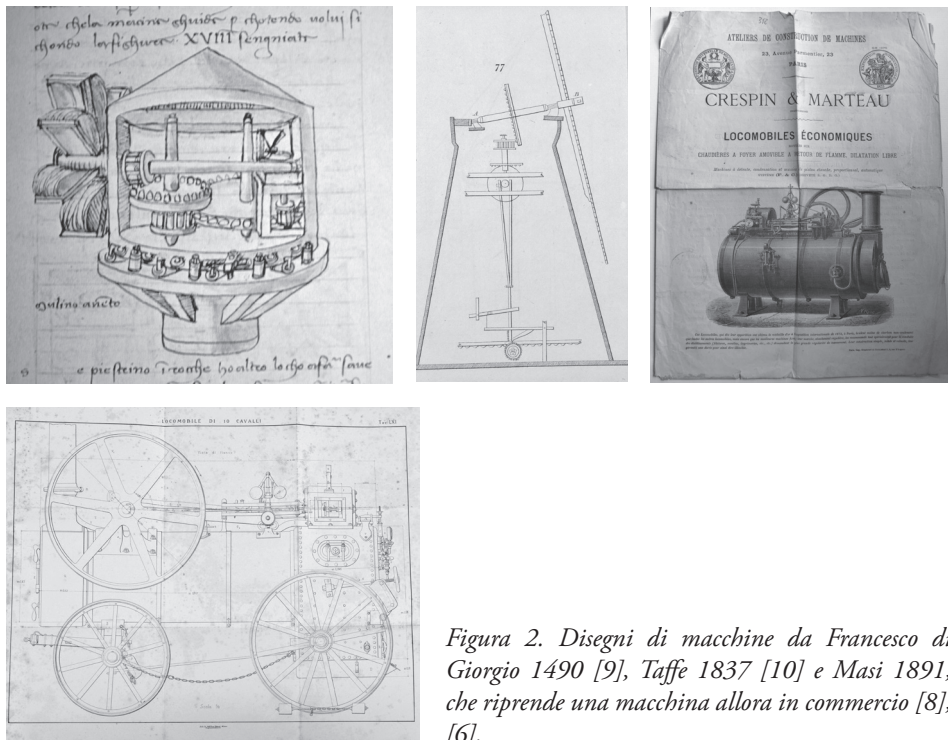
Disegni di macchine da Francesco di Giorgio 1490 [9], Taffe 1837 [10] e Masi 1891, che riprende una macchina allora in commercio [8], [6].
